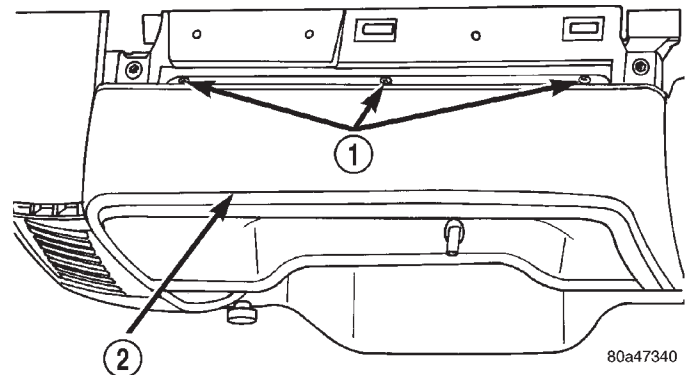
Desmontaje e instalación de los tornillos superiores del marco del grupo de instrumentos
